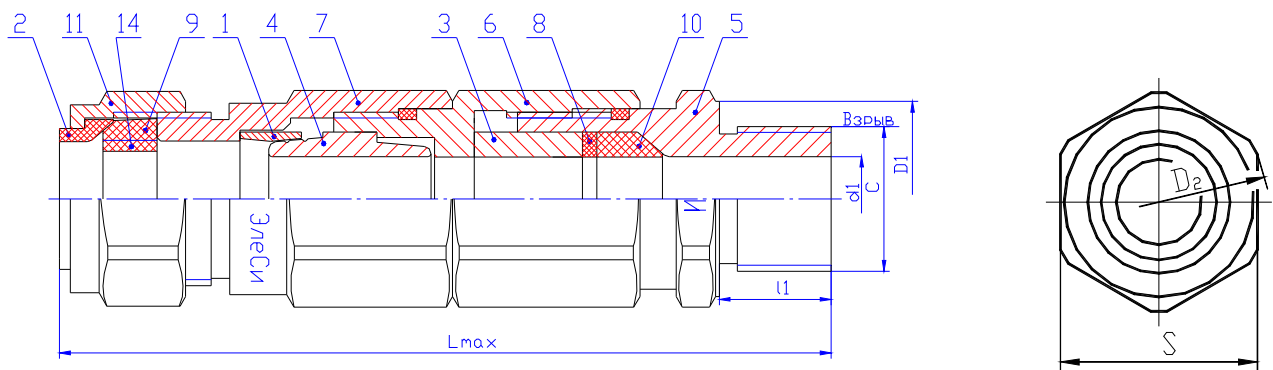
Конструкция кабельного ввода для монтажа бронированного кабеля
